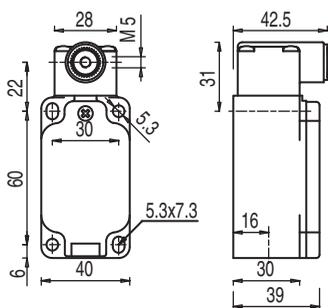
Dimensions des S300-P13C1-M20-SB et S300-P13C1-M12-SB en mm
